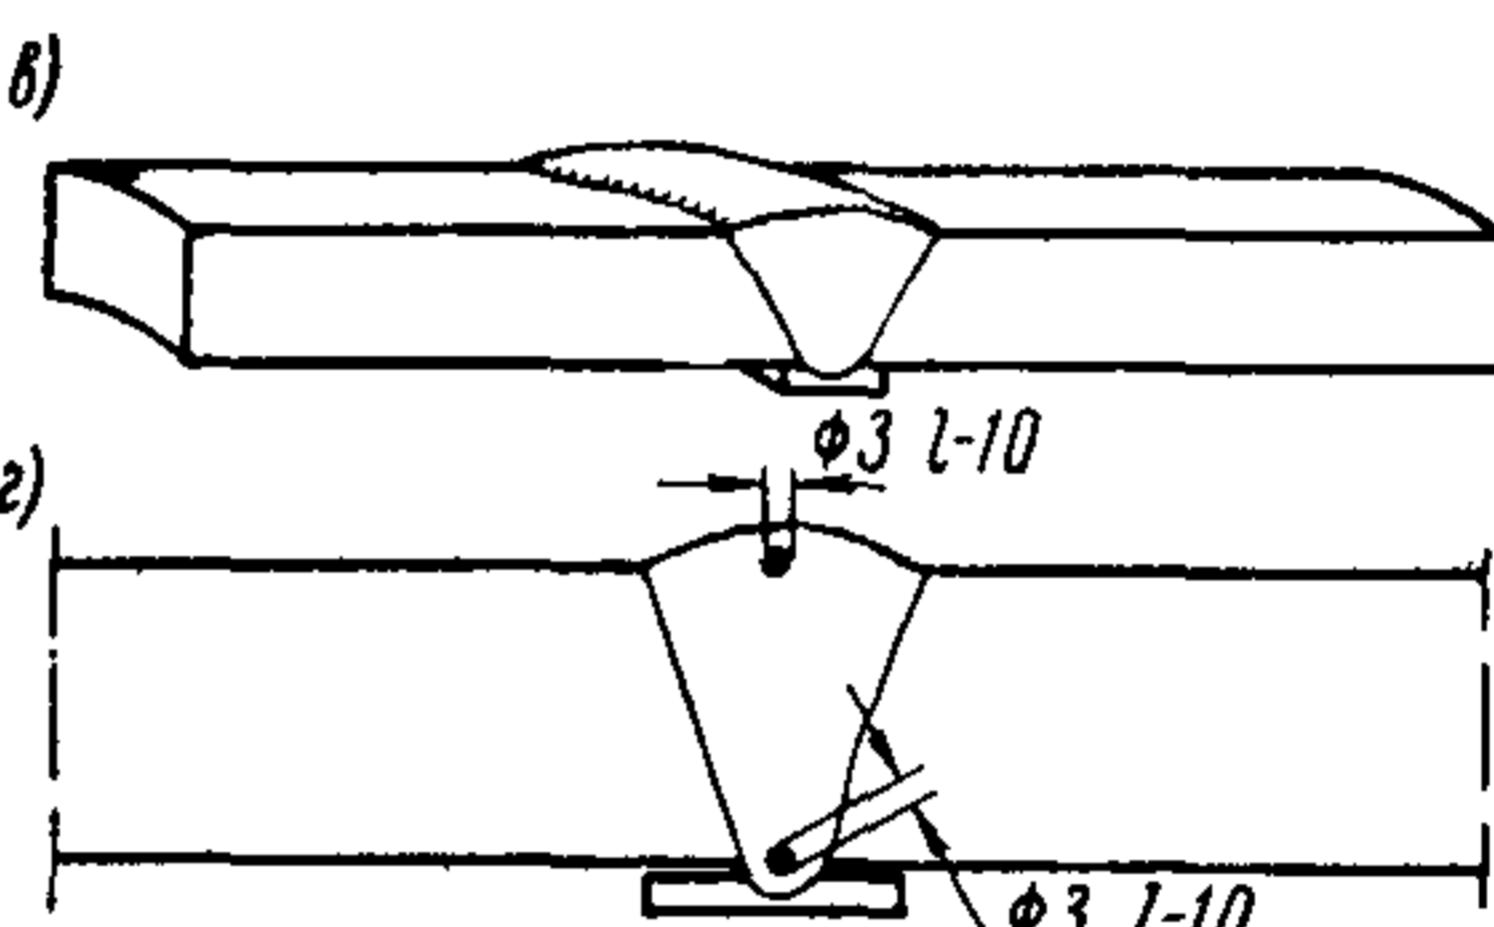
Изготовление эталонных образцов из обрезка трубы
